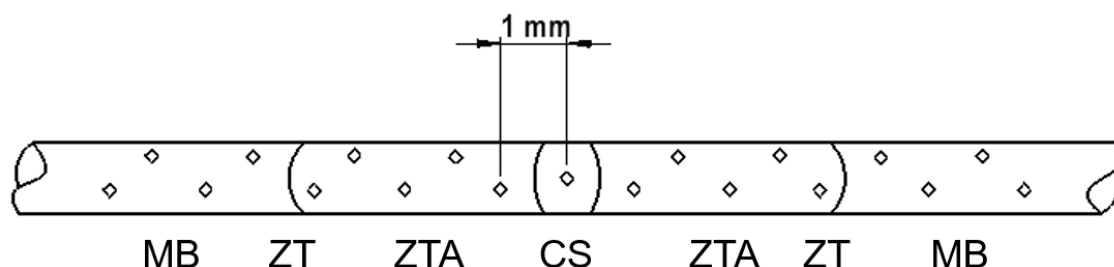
Ilustração do perfil “dente de serra” passando pelas diferentes microestruturas do arame soldado. Metal base (MB) zona de transição (ZT), zona termicamente afetada (ZTA) e centro de solda (CS).
